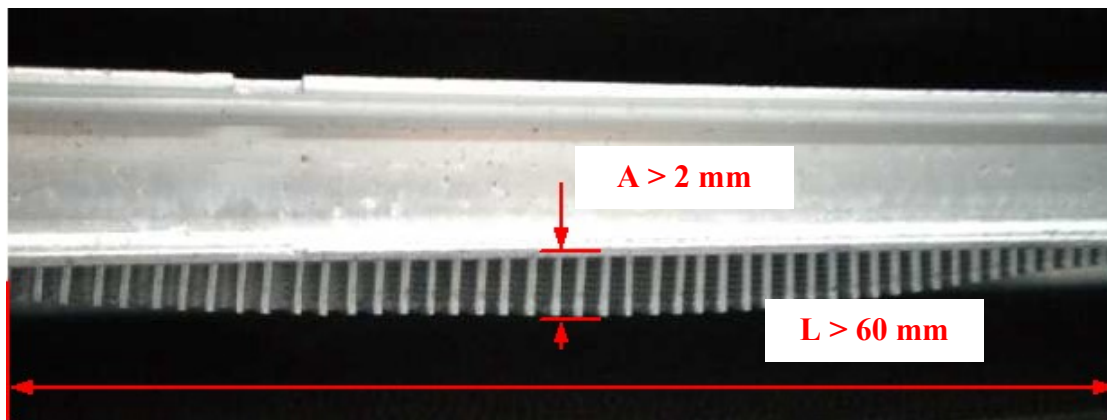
aletta caduta rispetto al fianchetto non accettabile
